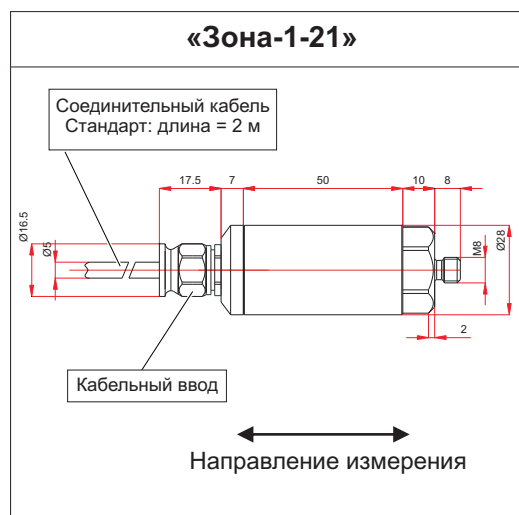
Размеры корпуса и направление измерения: «Зона-1-21»
